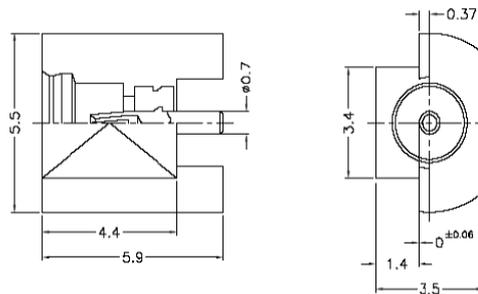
Dimensiones físicas del conector de antena del Módulo Motorola G24.
